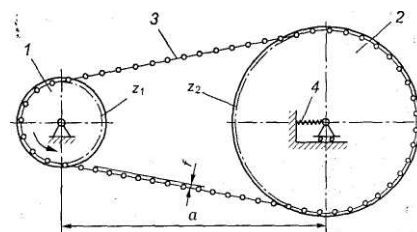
Цепная передача: 1 – ведущая звёздочка; 2 – ведомая звёздочка; 3 – цепь; 4 – натяжное устройство
